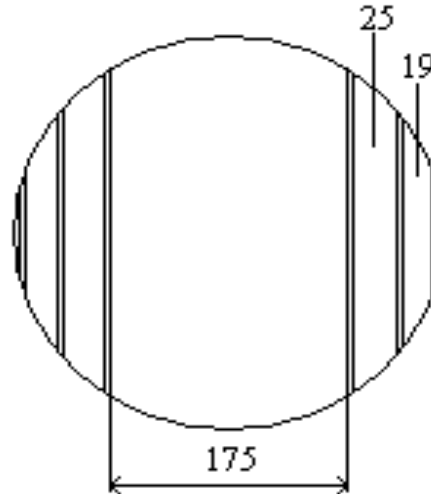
Схема розкрою лісоматеріалу круглого на необрізні пиломатеріали та брус (I прохід)
